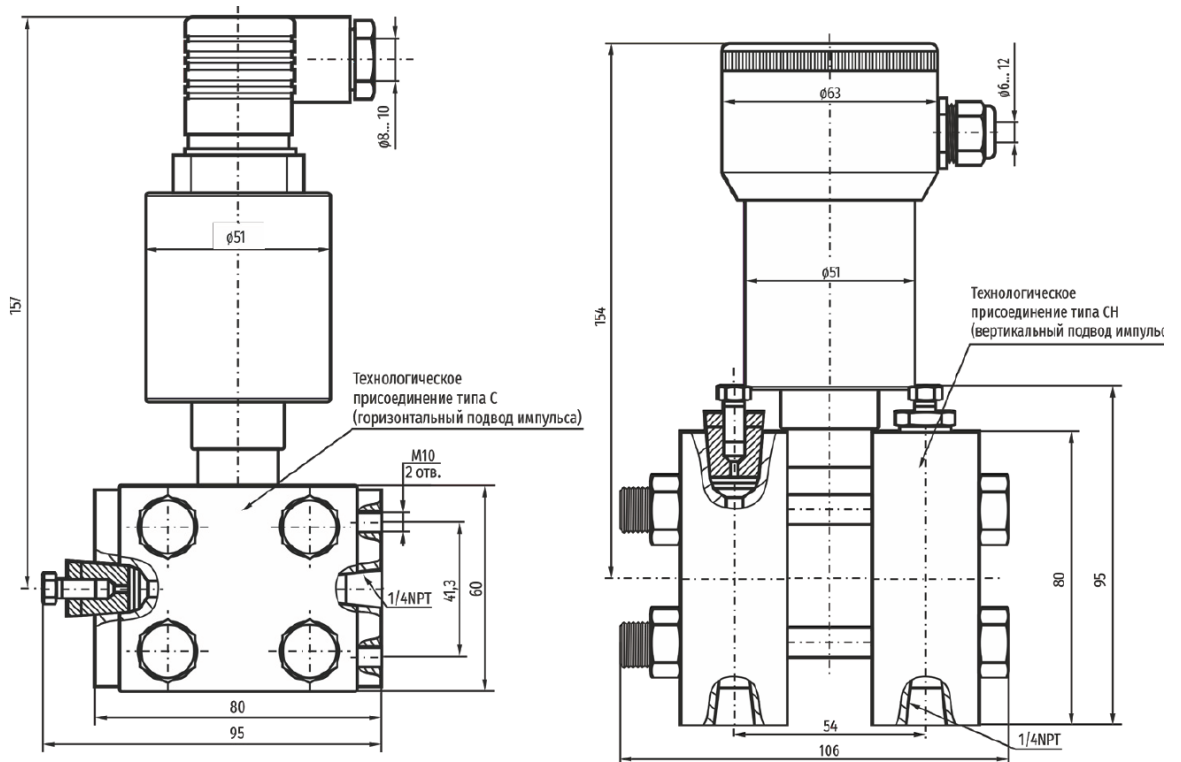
Преобразователь давления измерительный APR-2000 с типами процессного присоединения С и СН. Внешний вид и габаритные размеры
